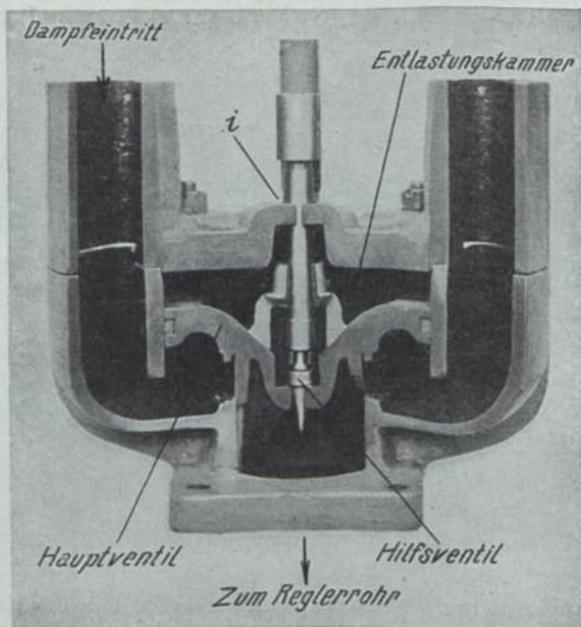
Ventilregler Bauart Fritz Wagner & Co.
